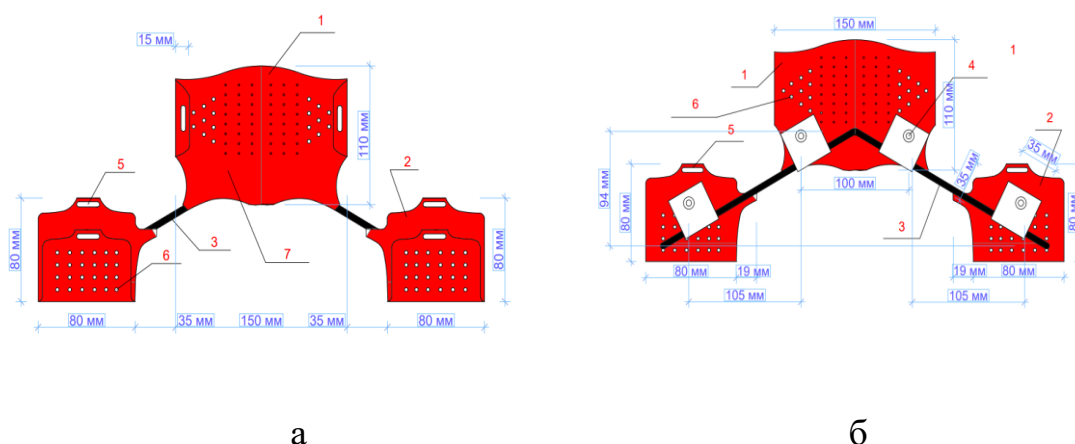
Схема динамической шины: а - вид спереди; б - вид сзади. Обозначения: 1 - корпус из формоустойчивой пластмассы, 2 - бедренные манжеты, 3 - распорка угольной формы, 4 - триплексные фиксаторы с болтовым соединением, 5 - петли для проведения ремней, 6 - отверстия на теле корпуса для вентиляции кожи.
